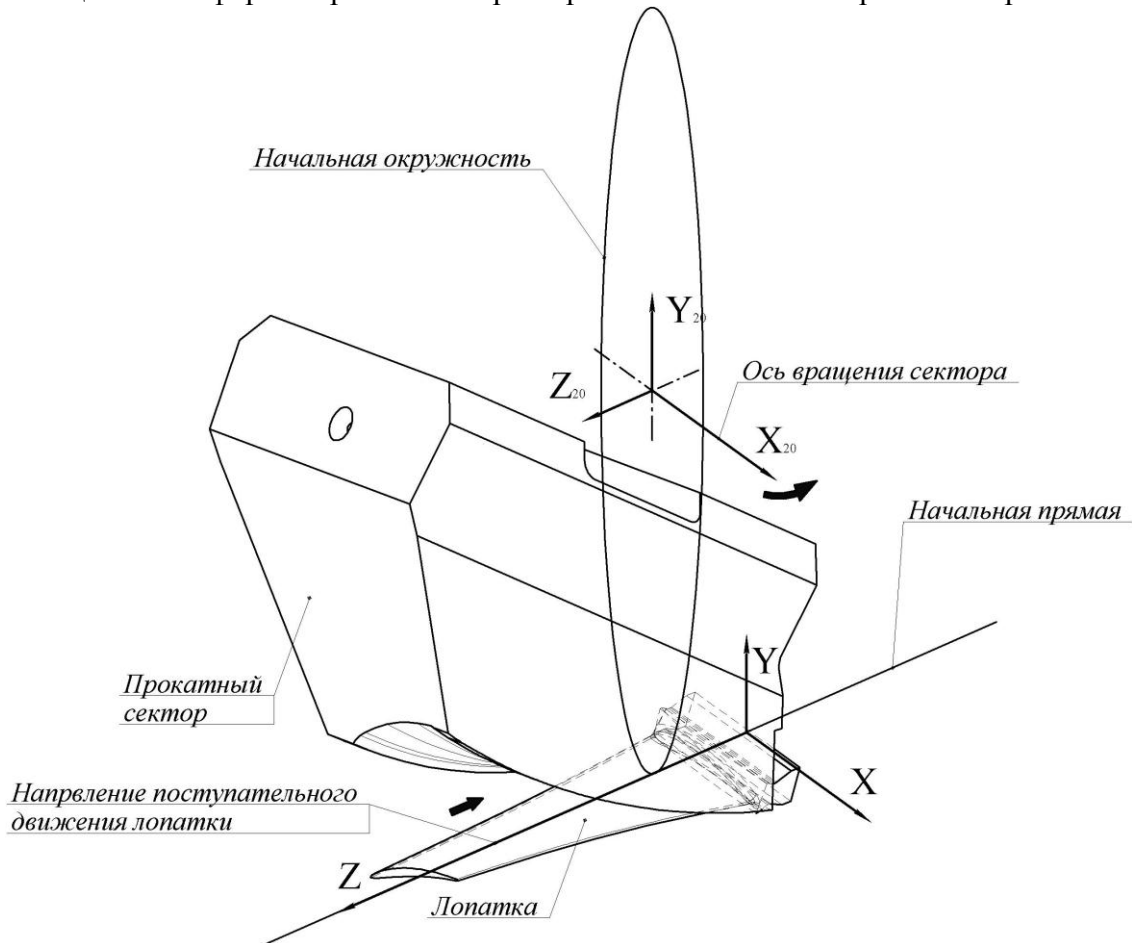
Общая схема формообразования при обработке поверхности корыта лопатки.
